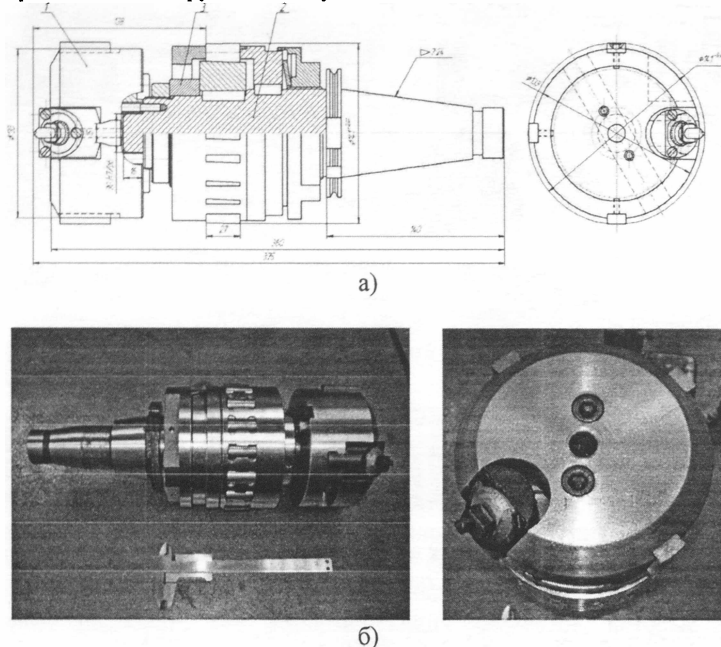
Комбинированный инструмента: а) сборочный чертеж ; б) общий вид
